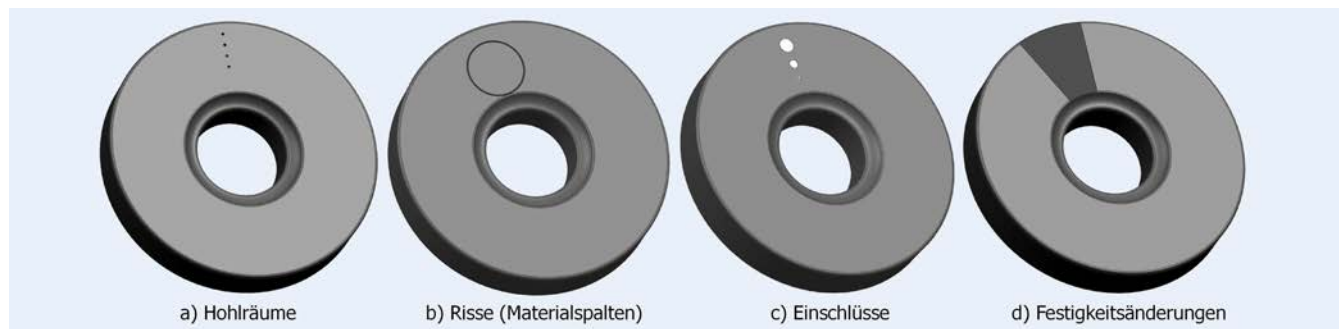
Versuchsrohlinge mit künstlich eingebrachten Bauteilfehlern. Bild: Institut für PTW
